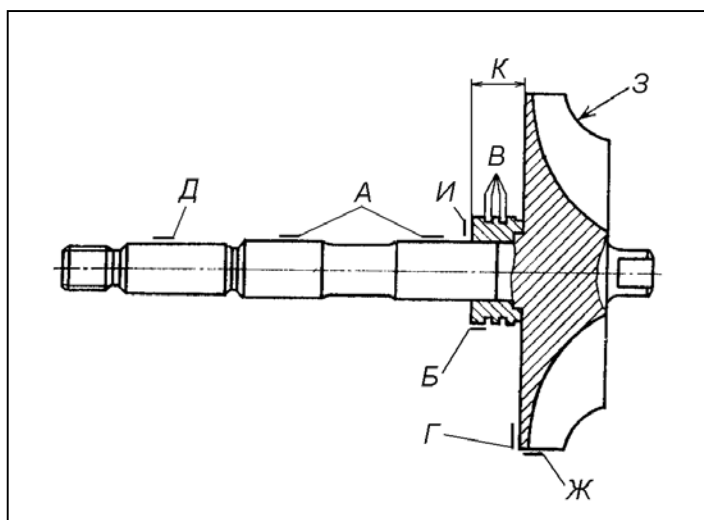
Вал ротора с колесом турбины в сборе (на рисунке показан эскиз условного типового вала)
